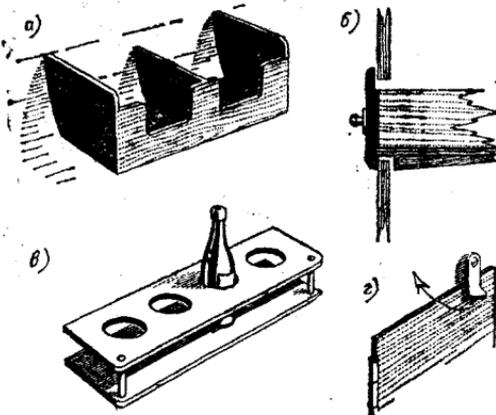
Детали оборудования каюты: а — полка для посуду; б — стопор для выдвижного ящика; в — полочка для бутылок и стаканов; г — стопор для двери шкафа.
